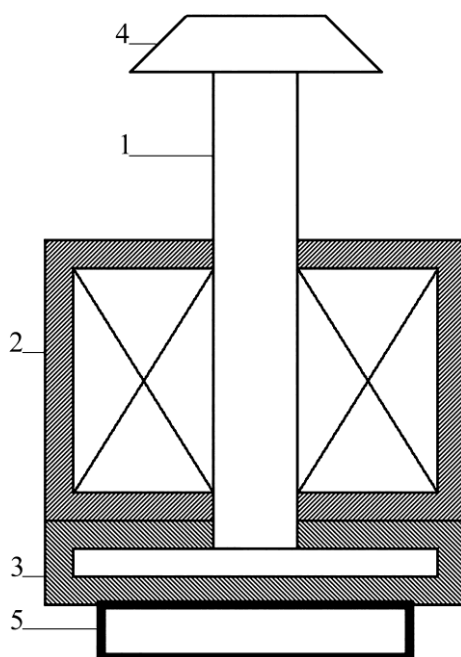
Электромагнит для захвата обрабатываемой детали: 1 – стержень; 2 – электромагнитная катушка; 3 – водоохлаждаемая пластина; 4 – коническая шестерня; 5 – обрабатываемая деталь [127].
